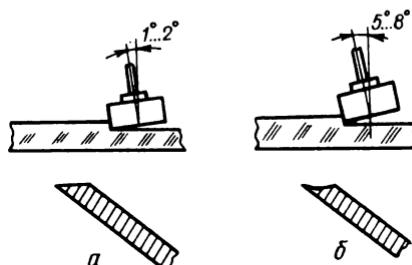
Схема выверки ножа на столе ножеточного станка:
